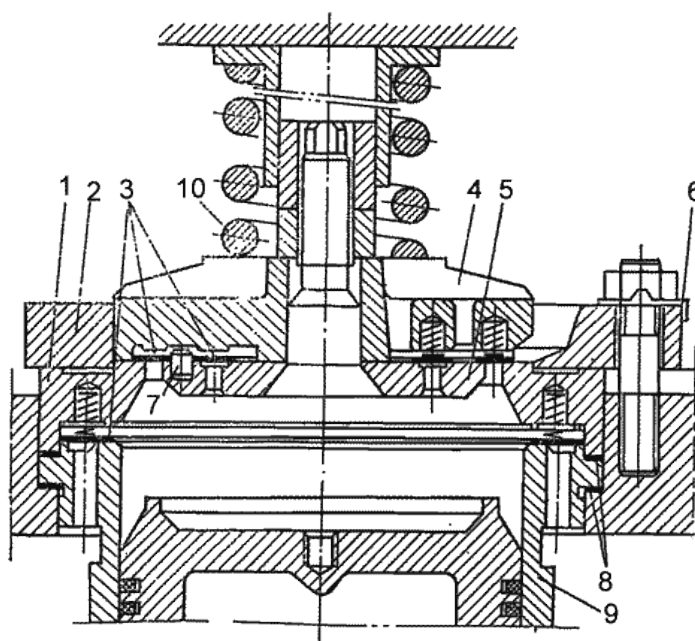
Клапанна група компресора: 1 - корпус всмоктувального клапана; 2 - напрямна всмоктувального клапана; 3 - кільцеві пластини; 4 – розетка нагнітального клапана; 5 - сідло нагнітального клапана; 6 – стопорна шайба; 7 – штифт; 8 – прокладки паронітові; 9 – гільза циліндрова; 10 - пружина буферна хибної кришки.
